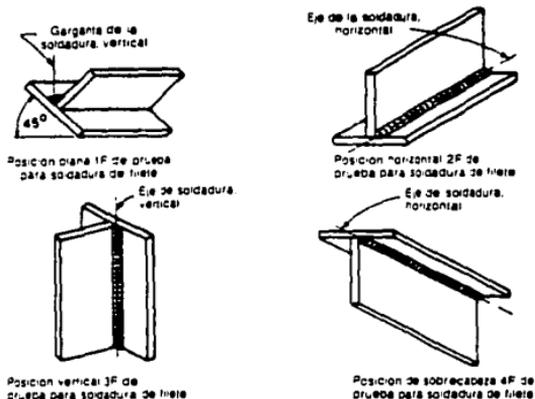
Posiciones para la calificación de soldadores en soldaduras de filete.
